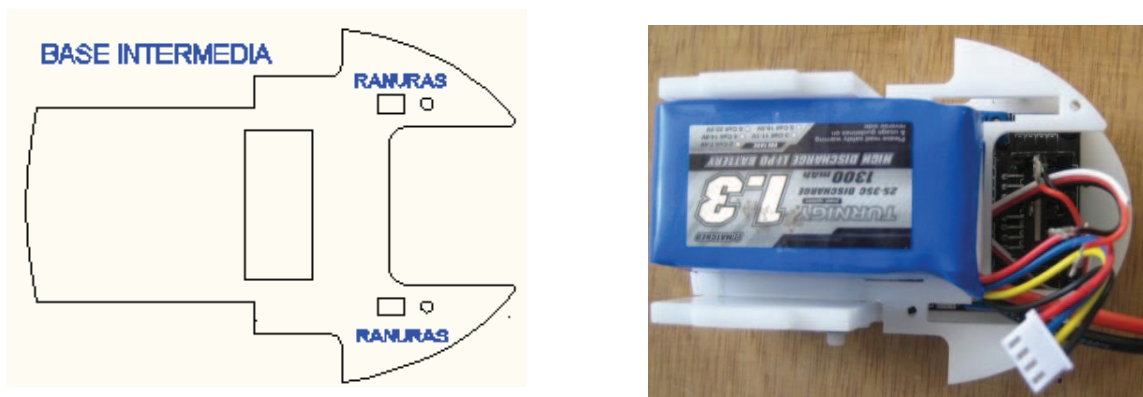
Izquierda) Base intermedia dibujada en AUTOCAD, derecha) Base intermedia ensamblada vista superior
